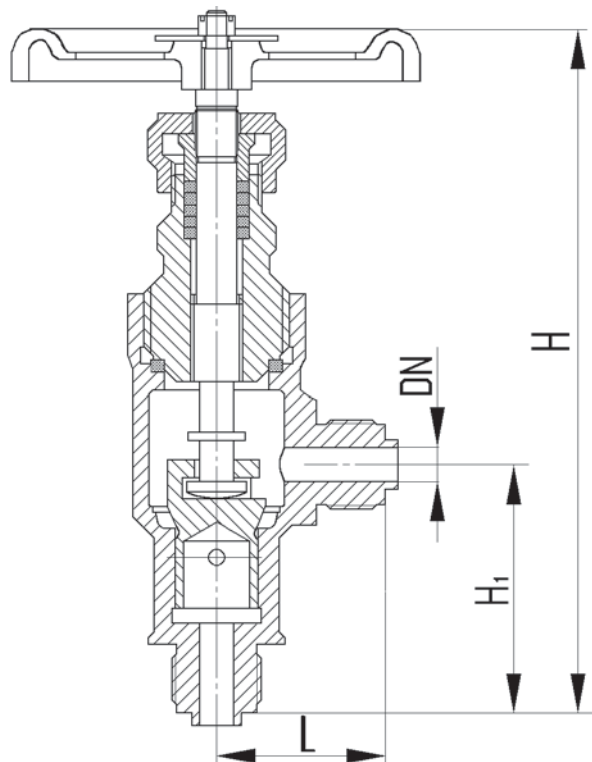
Клапан дроссельный угловой штуцерный
